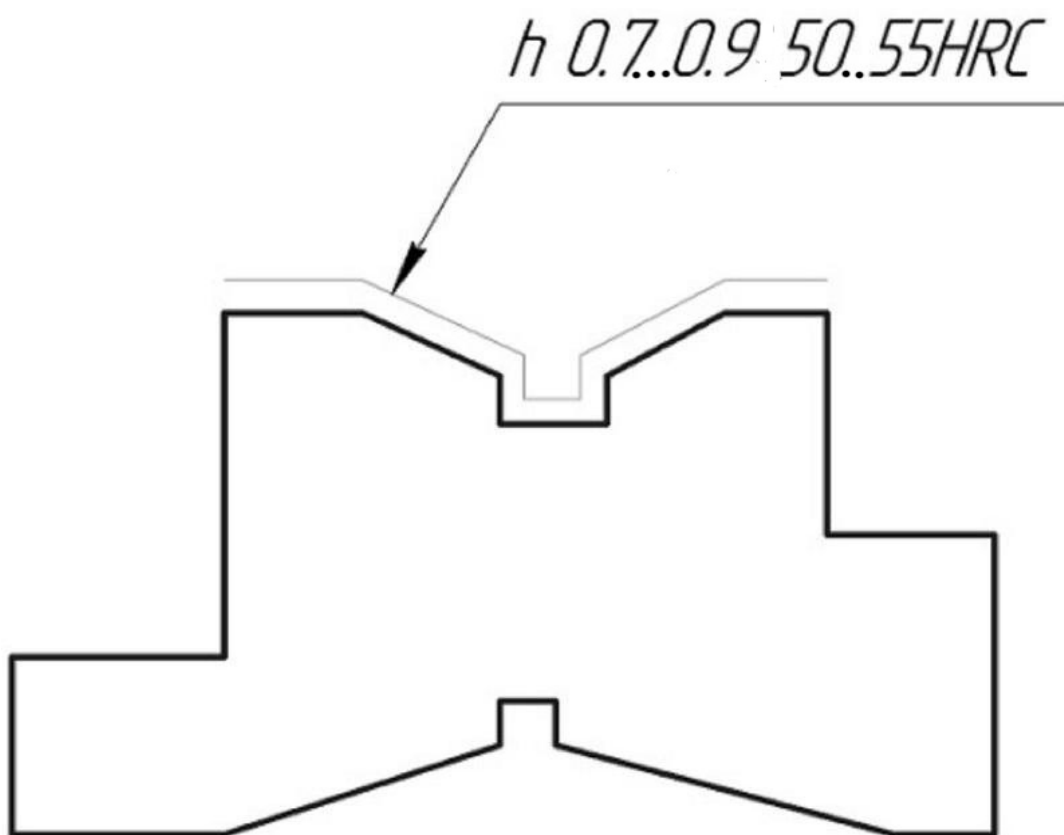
Указание поверхности, отличающейся по твердости от остальных поверхностей детали
